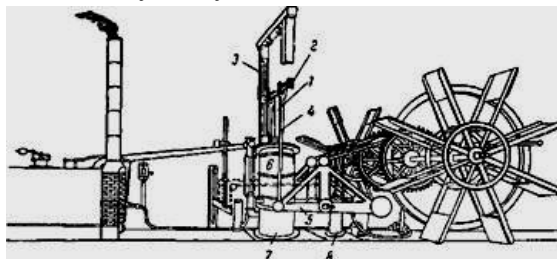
Устройство двигателя парохода «Клермонт»: 1 – шток; 2 – кресткопф; 3 – направляющая; 4 – шатун; 5 – балансиры; 6 – поршень; 7 – цилиндр.
